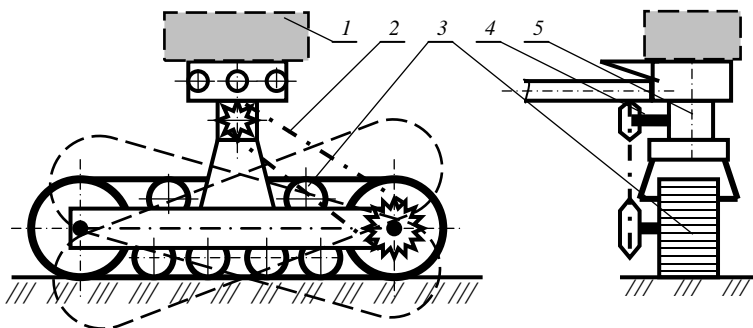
Схема вспомогательной гусеницы: 1 - противовес; 2 - цепная передача; 3 - вспомогательная гусеница; 4 - ведущий вал; 5 - поворотная головка
